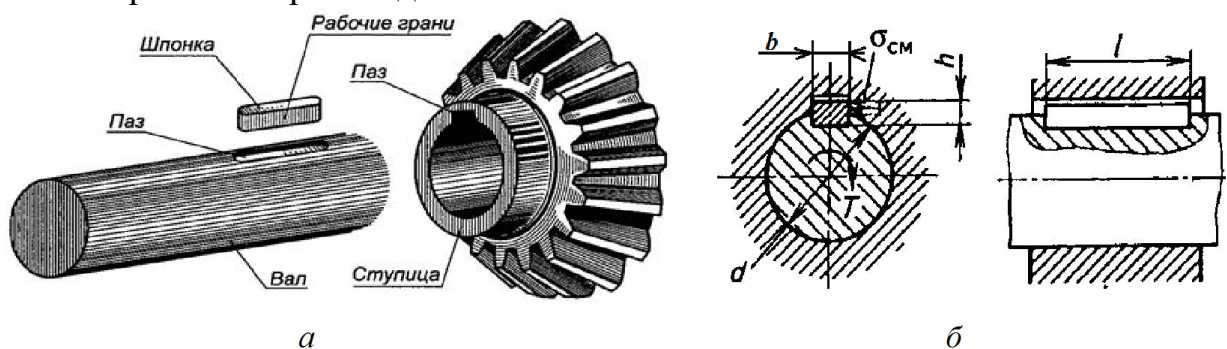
Шпоночное соединение детали с валом: *а* – конструкция; *б* – чертеж
